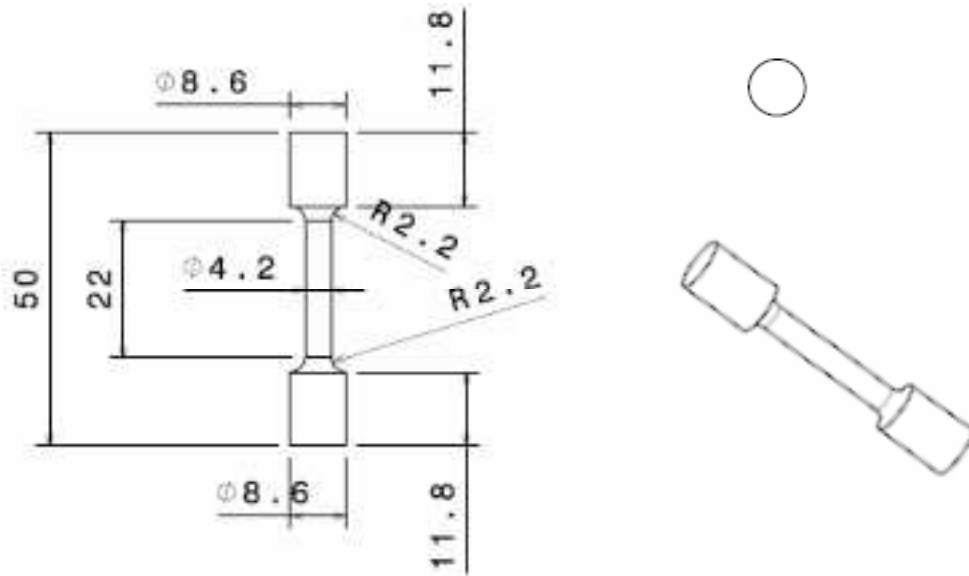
Plan des éprouvettes de traction – Dimensions en mm
